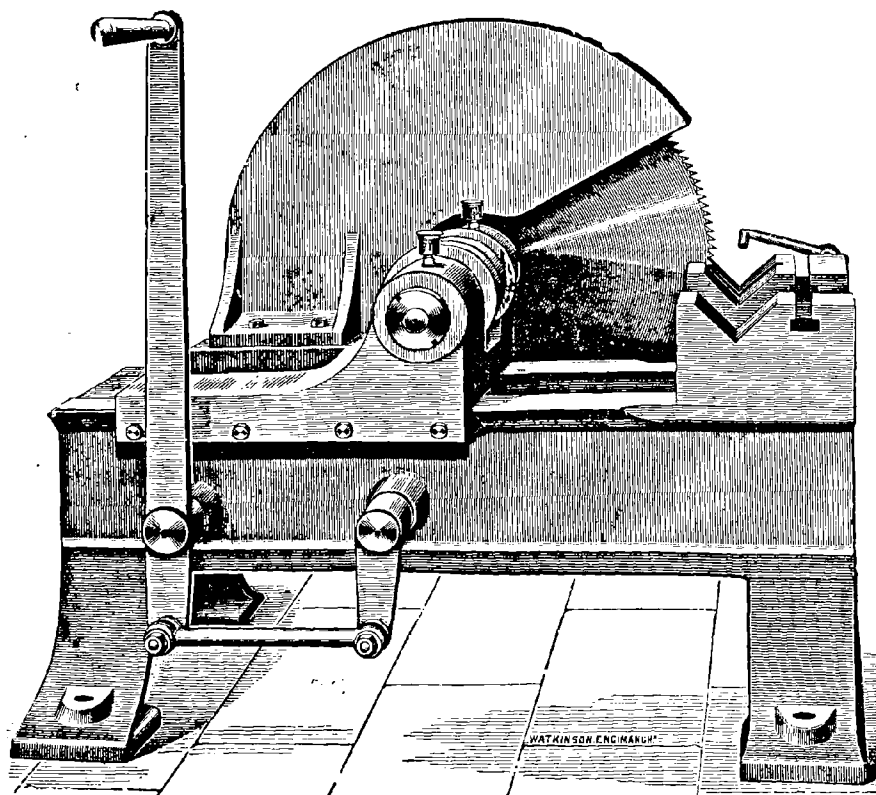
Machine à scier les métaux à chaud de M. Lucas.
